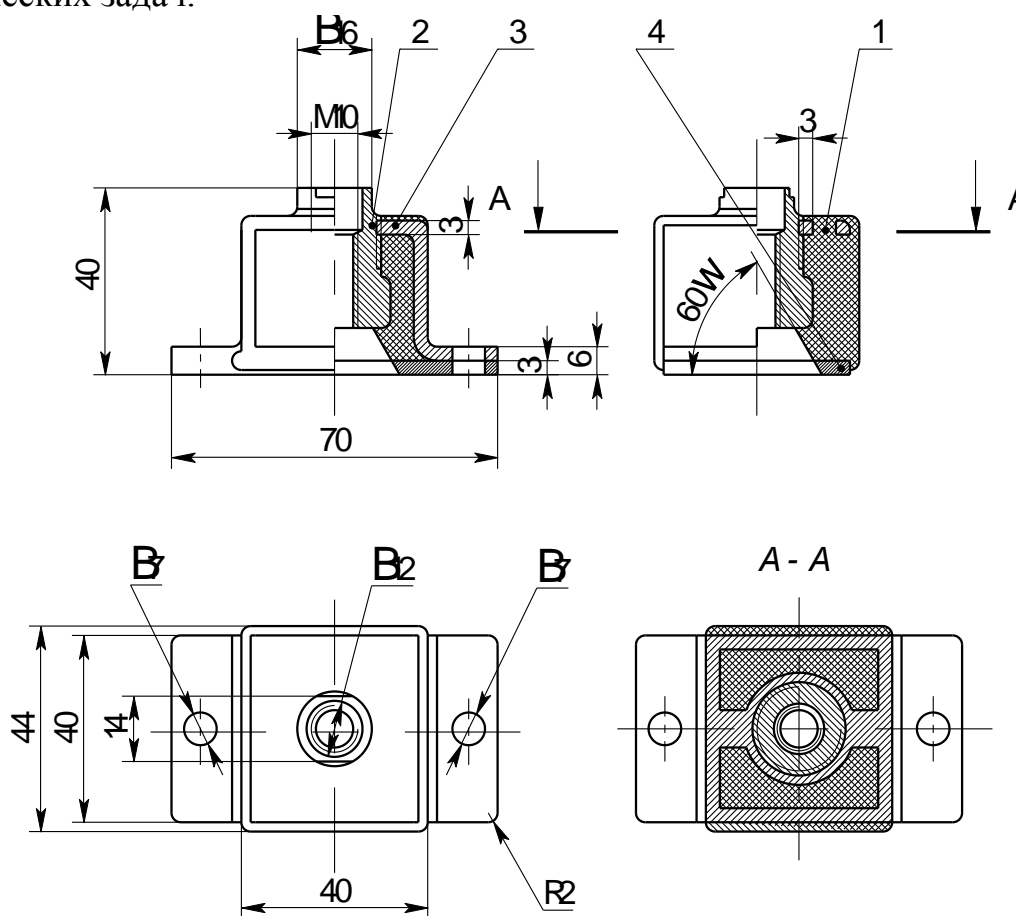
Двухмерная модель изделия: 1 – корпус; 2 – втулка; 3 – скоба; 4 – пластина.
